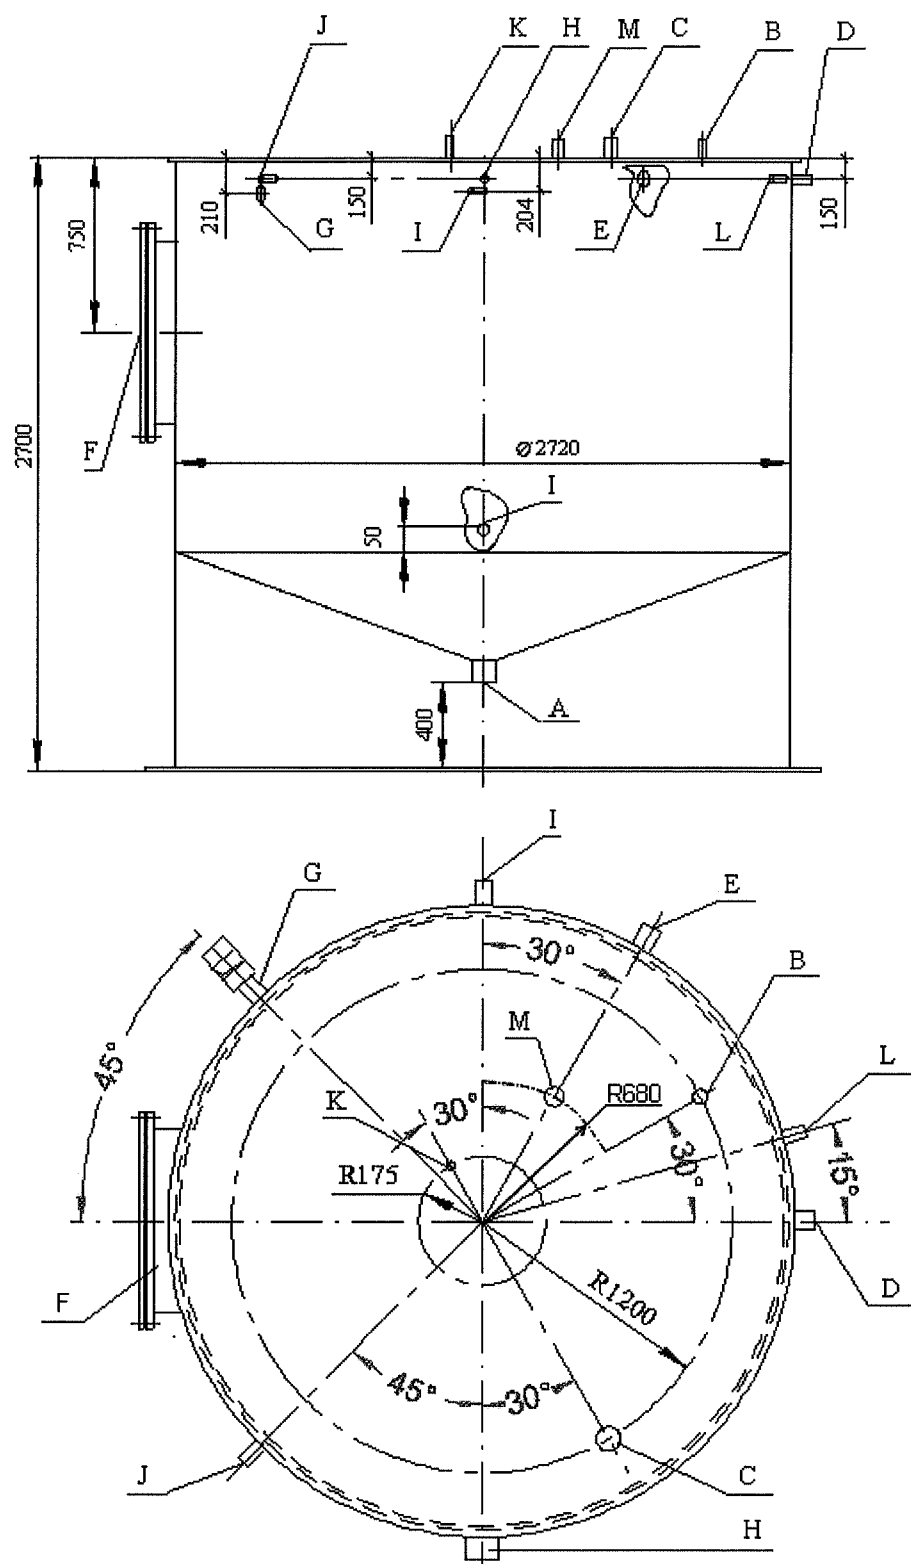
Габаритный чертеж бака боросодержащих дренажей
